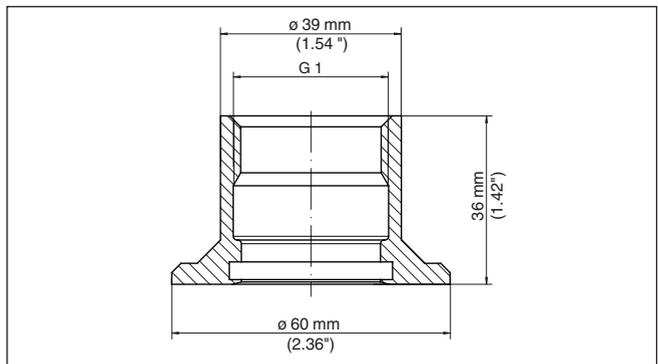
Medidas racor para soldar G1 (DIN 3852-A)
